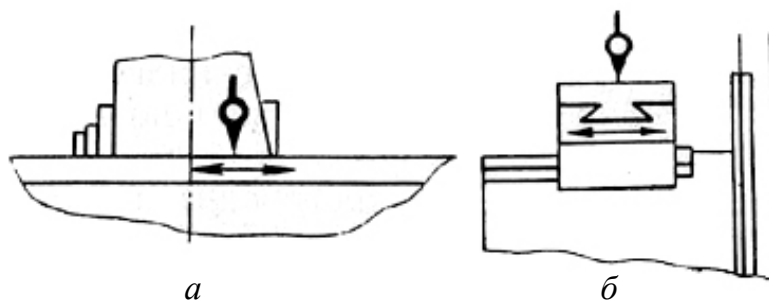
Проверка параллельности рабочей поверхности стола направлению его перемещения: а – продольного; б – поперечного
